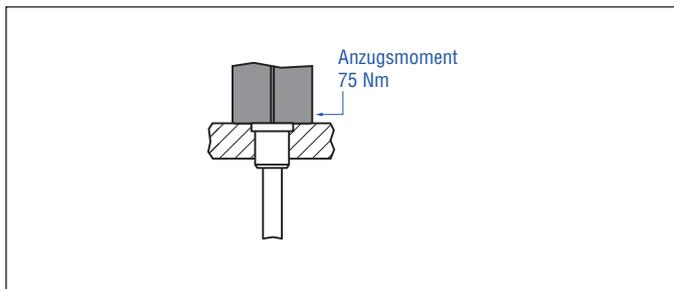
Einbaubeispiel für Gewindeflansch »F«, »M«, »S«, »W«
